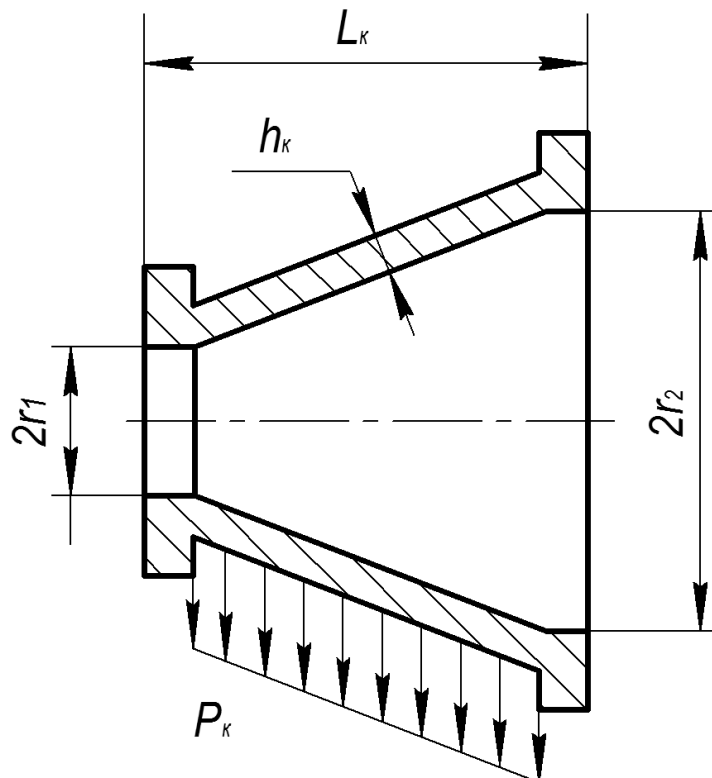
Схема навантаження конічної обичайки ротора центрифуги
